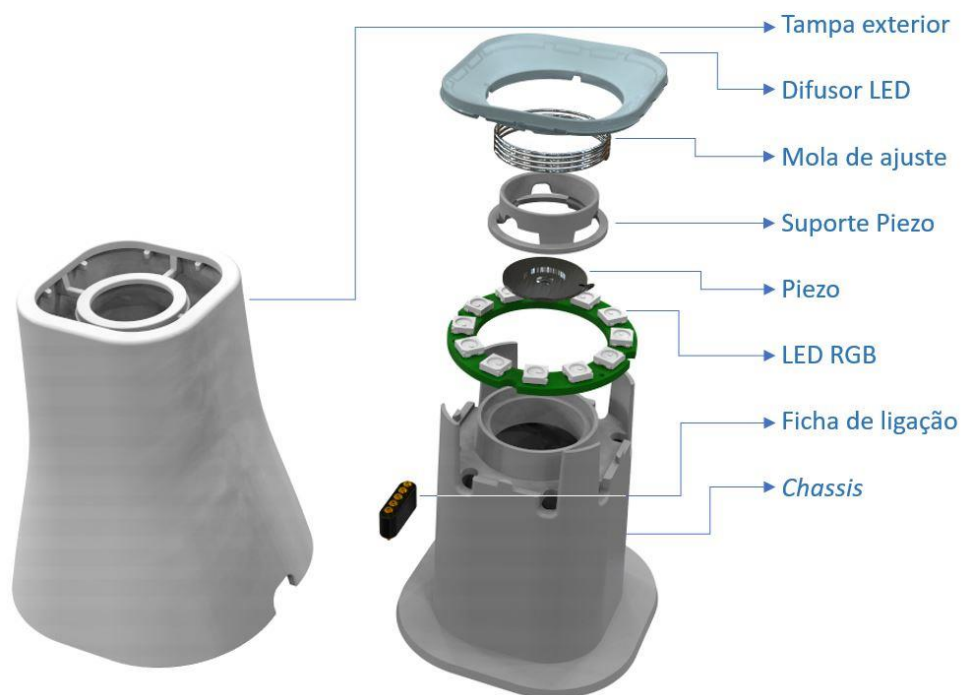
Vista explodida dos componentes principais do topo do dispositivo de difusão
